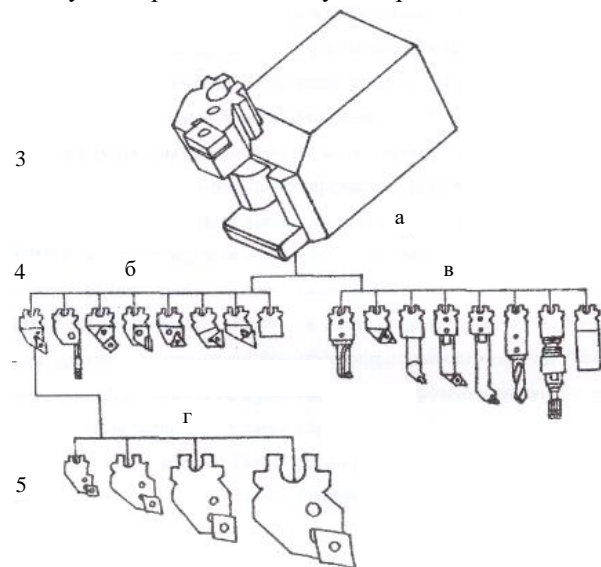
Модульная система инструментов для токарных станков фирмы «Сандвик Коромант» (Швеция): а) – корпус с узлом крепления модулей; б) – виды модулей для наружного точения; в) – виды модулей для обработки отверстий; г) – размерный ряд одного вида
